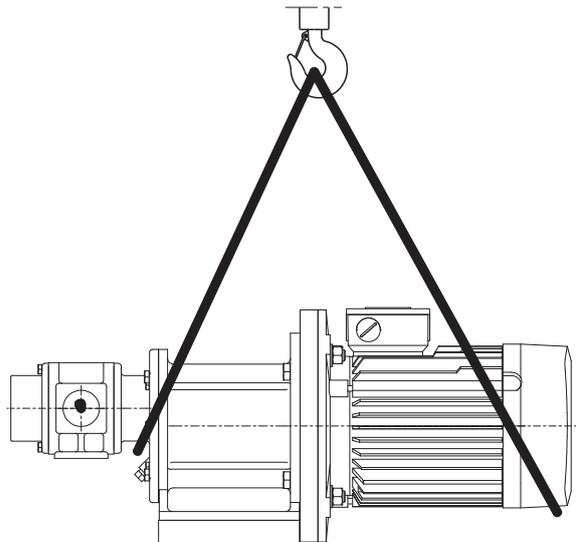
Hebezeug befestigen an Pumpe ohne Grundplatte
